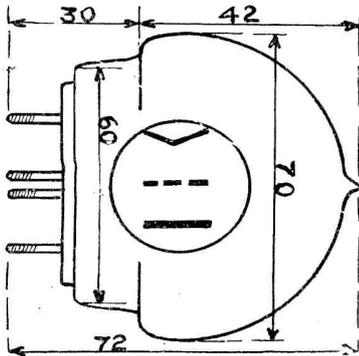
Silhouette, dimensions du tube triode émetteur 316 A Western.
